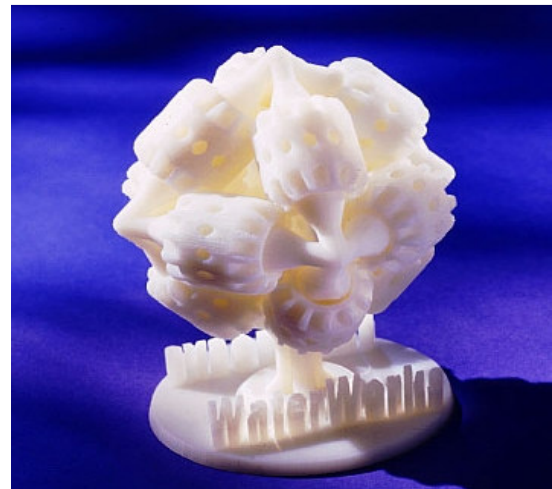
Peça construída em um único bloco com remoção de material de suporte por ultra-som
